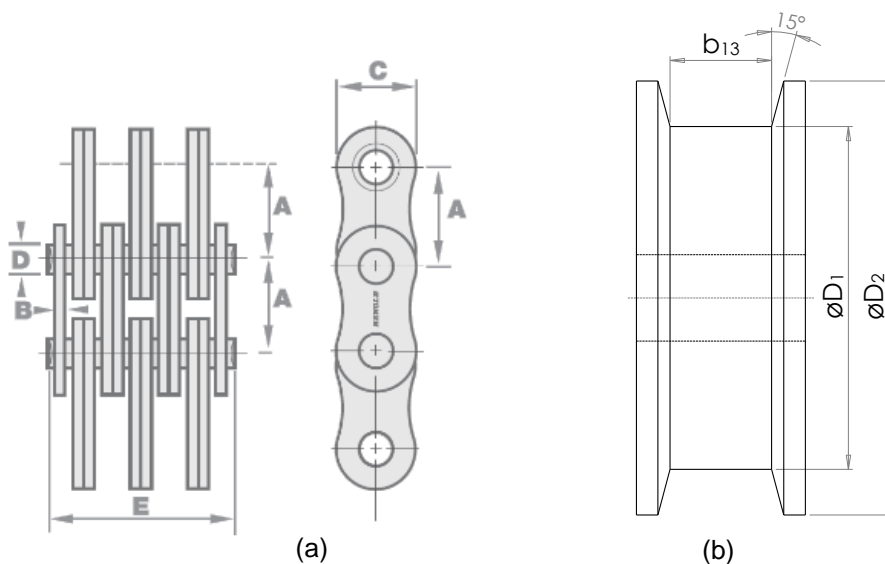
Dimensiones: a) Cadena; b) Polea
